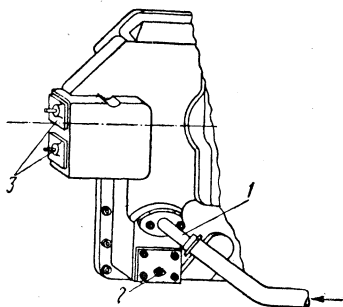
Подсоединение патрубка от постороннего насоса для прокачки двигателя маслом: 1 — патрубок с фланцем; 2 — пробка для слива смазки; 3 — масляные пластинчатые фильтры
